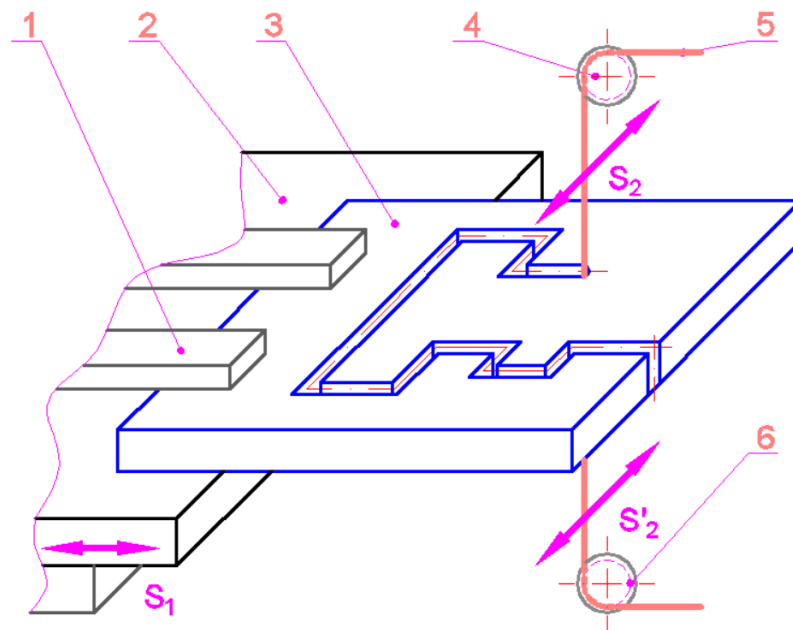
Кінематична схема електроерозійної обробки дротяним електродом-інструментом: 1 – затискач; 2 – робочий стіл електроерозійного верстата; 3 – електрод-заготовка; 4 – верхній напрямний ролик дротяного електроду-інструменту; 5 – дротяний електрод-інструмент; 6 – нижній напрямний ролик дротяного електроду-інструменту;  $S_1$  – рух подачі столу;  $S_2$  та  $S'_2$  – рух подачі дротяного електроду-інструменту (ванну з діелектричною робочою рідиною не показано)
